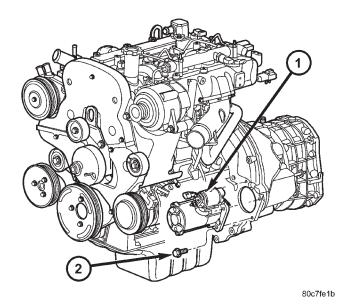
MOTOR DE ARRANQUE - MOTOR 2.5L DIESEL
